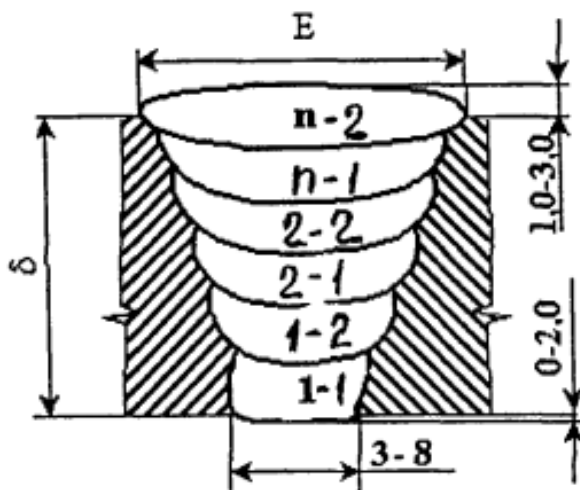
Схема наложения сварных валиков кольцевого сварного шва
